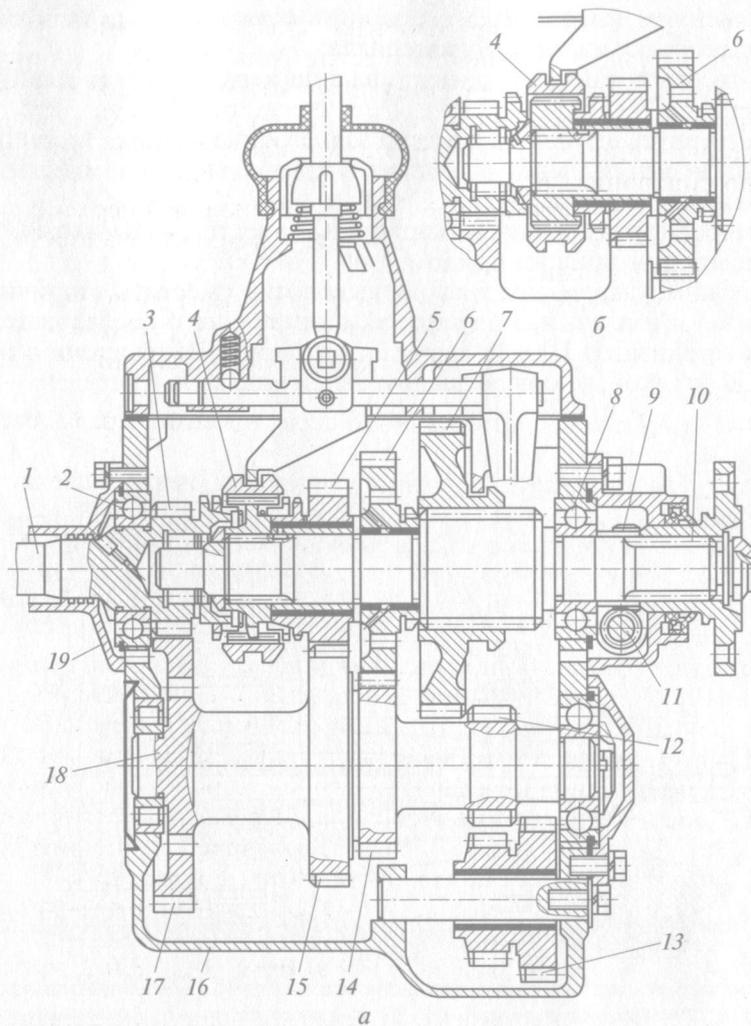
Четырехступенчатая коробка передач автомобилей ГАЗ-53А и ГАЗ-53-12:
